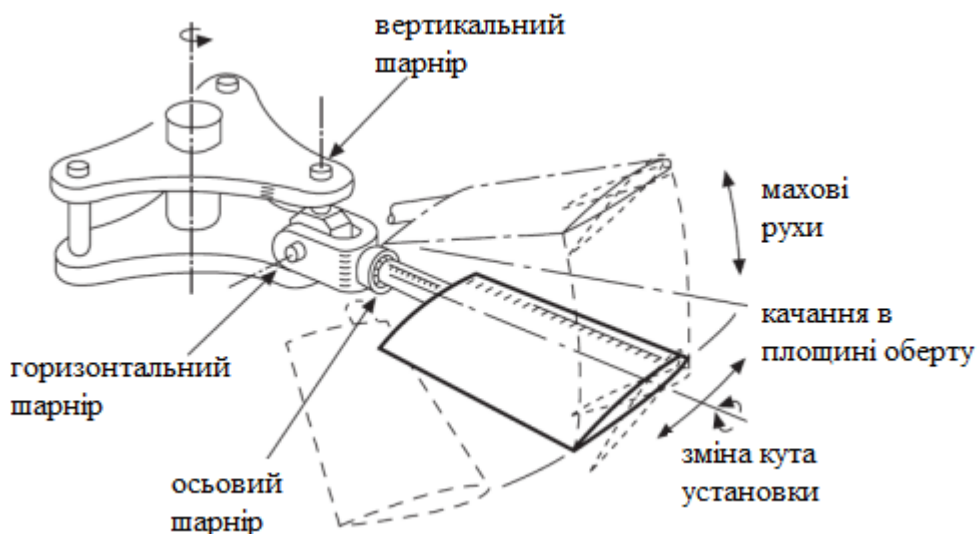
Схема шарнірної підвіски лопаті до втулки несучого гвинта
